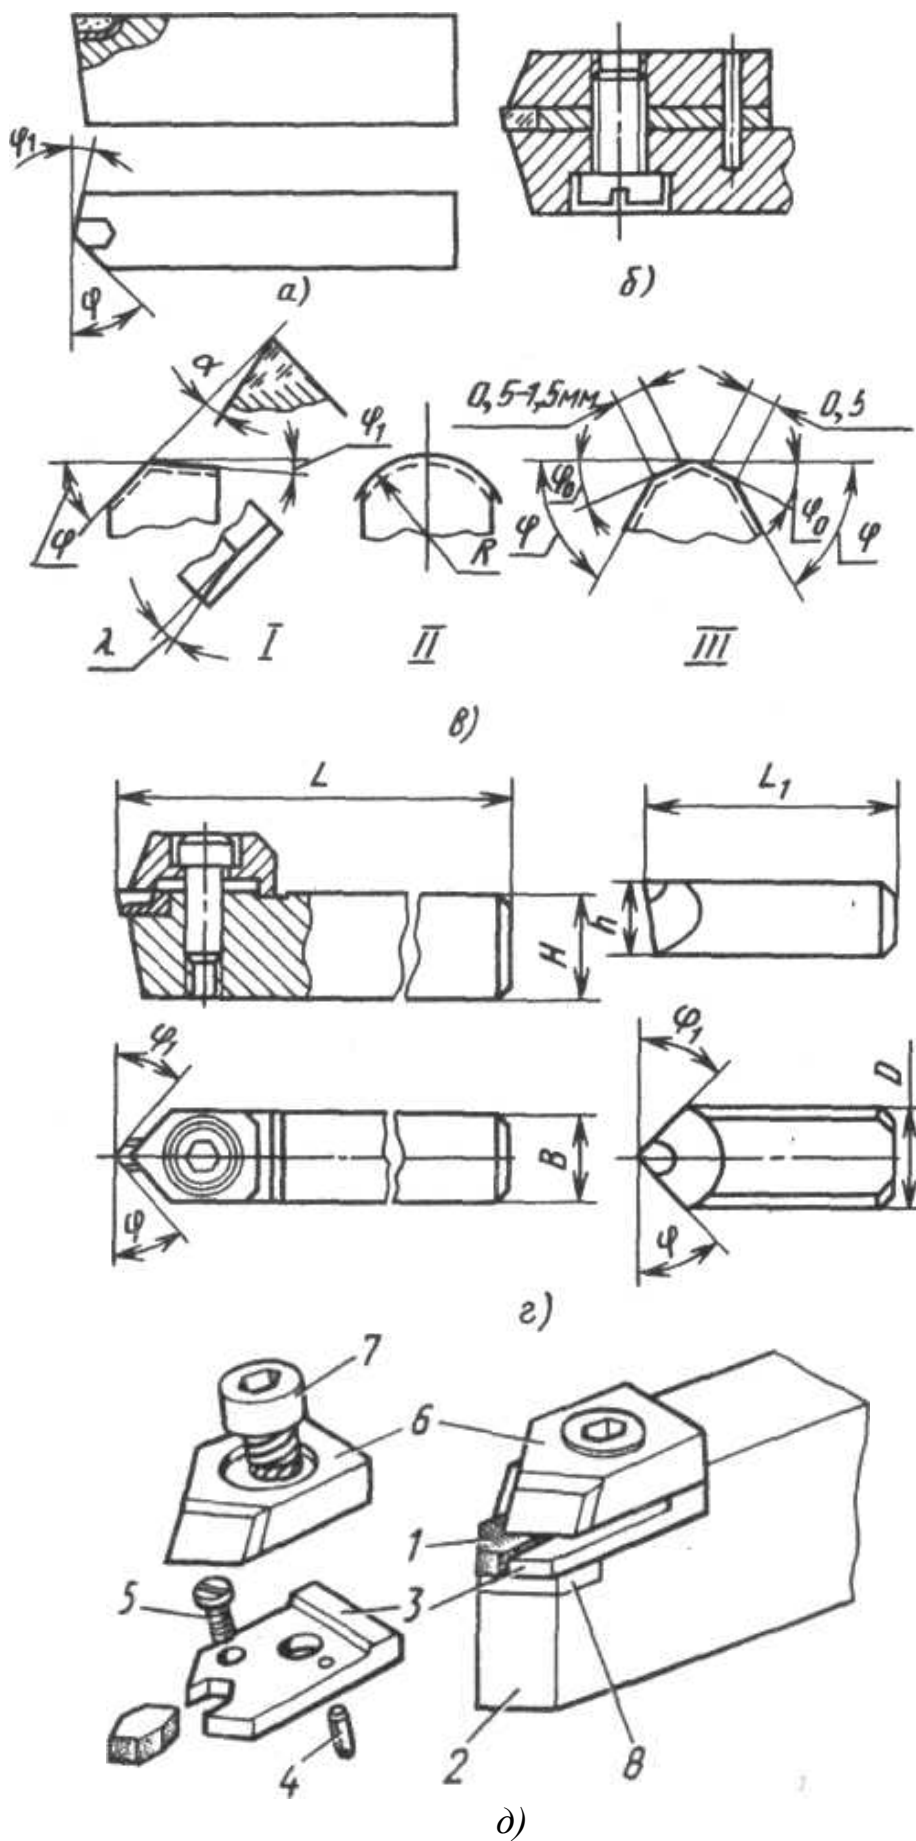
Конструкции резцов с режущими элементами из алмаза и композита
